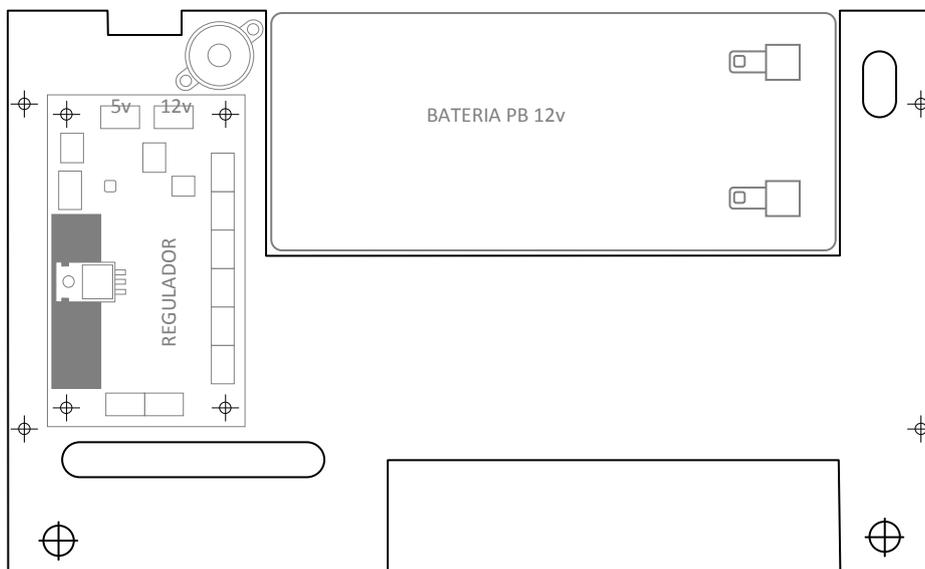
Vista en planta de la placa del segundo nivel, y colocación de los dispositivos. Escala aprox. 1:2.
